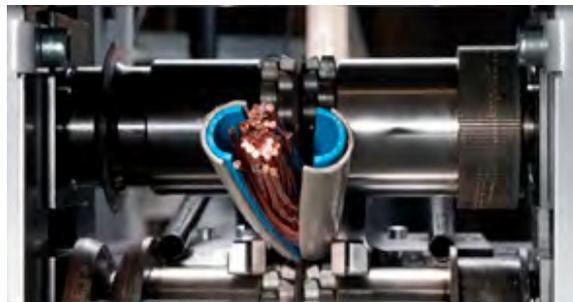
Работа кабелеразделочного станка с дисковыми ножами
